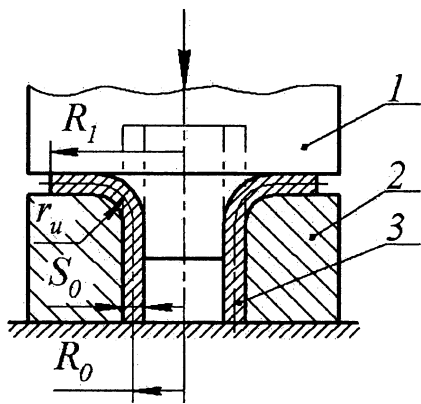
Схема отбортовки трубной заготовки: 1 - пуансон; 2 - матрица; 3 - заготовка
